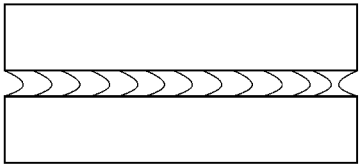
薄板对接 TIG 焊缝起弧和收弧豁口
